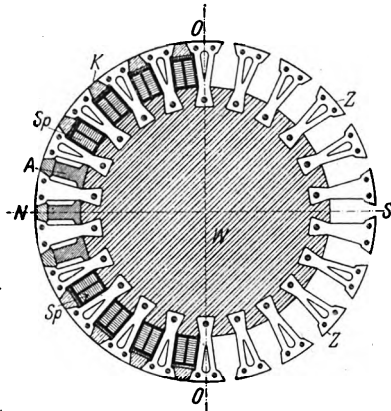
Feldmagnet für Turbodynamos mit eingesetzten Blechzähnen.
